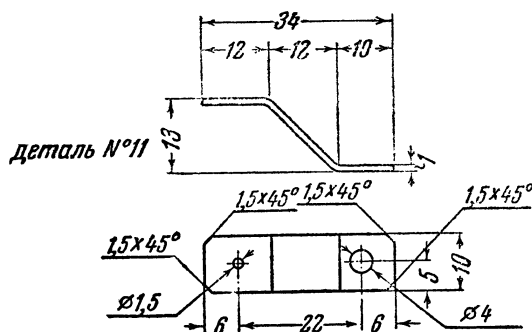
Кронштейн оси поводкового зубчатого колеса
